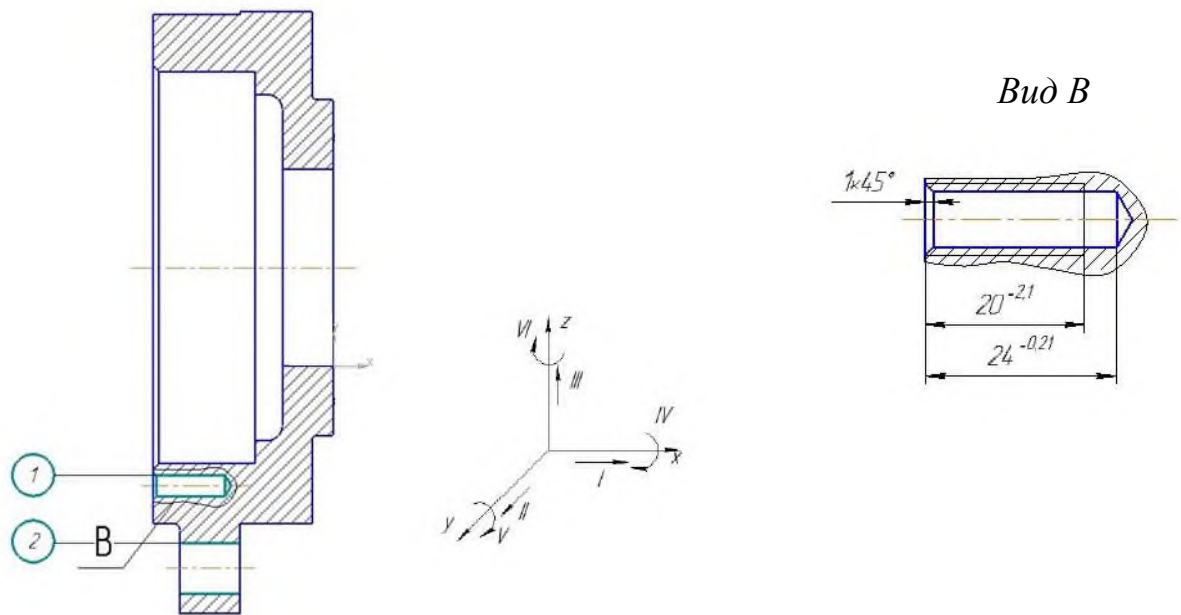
Ескіз обробки заготовки на операції 050
